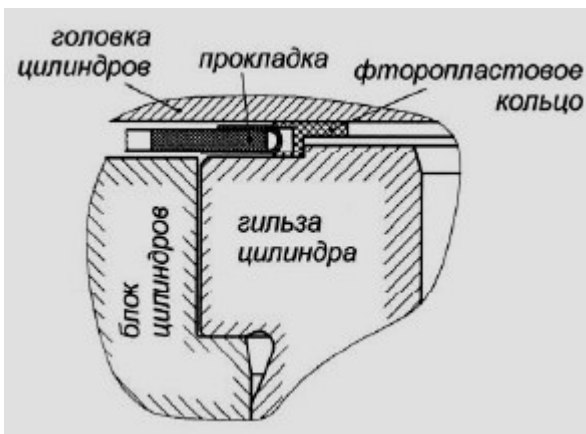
Схема установки уплотнителей в металлическую прокладку
